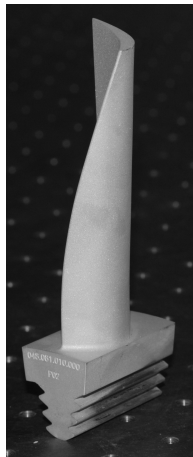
Turbinenschaufel für einen Luftturbinenprüfstand [4]
